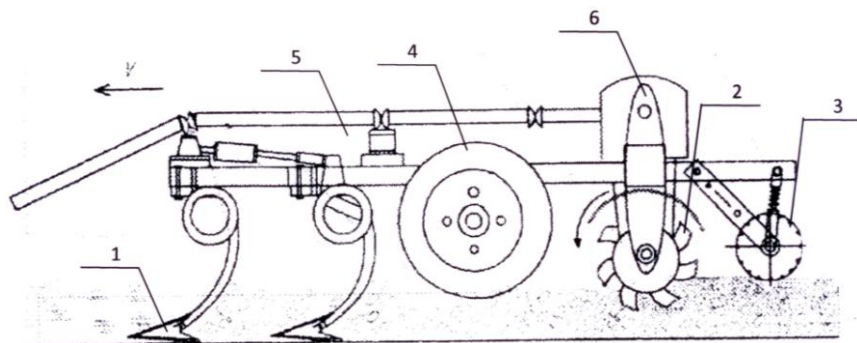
Комбинированный агрегат для подготовки почвы под посев с стрельчатыми и фрезерными рабочими органами и прикатывающим катком:
